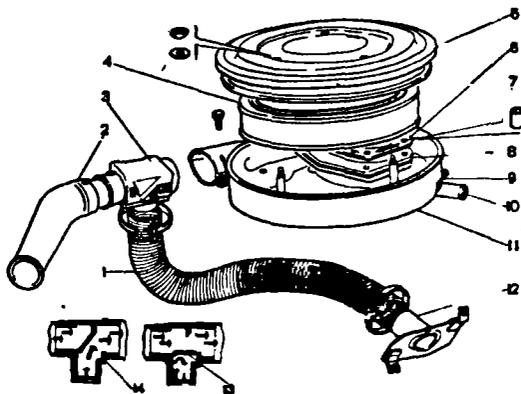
Детали воздушного фильтра: 1 - шланг воздухозаборника теплого воздуха; 2 - заборник холодного воздуха; 3 - терморегулятор; 4 - фильтрующий элемент; 5 - крышка; 6 - пластина крепления фильтра; 7 - дистанционная втулка; 8 - прокладка; 9 - патрубок для отвода картерных газов к золотниковому устройству карбюратора; 10 - вытяжной коллектор картерных газов; 11 - корпус воздушного фильтра; 12 - воздухозаборник теплого воздуха; 13 - заслонка терморегулятора; 14 - корпус терморегулятора
